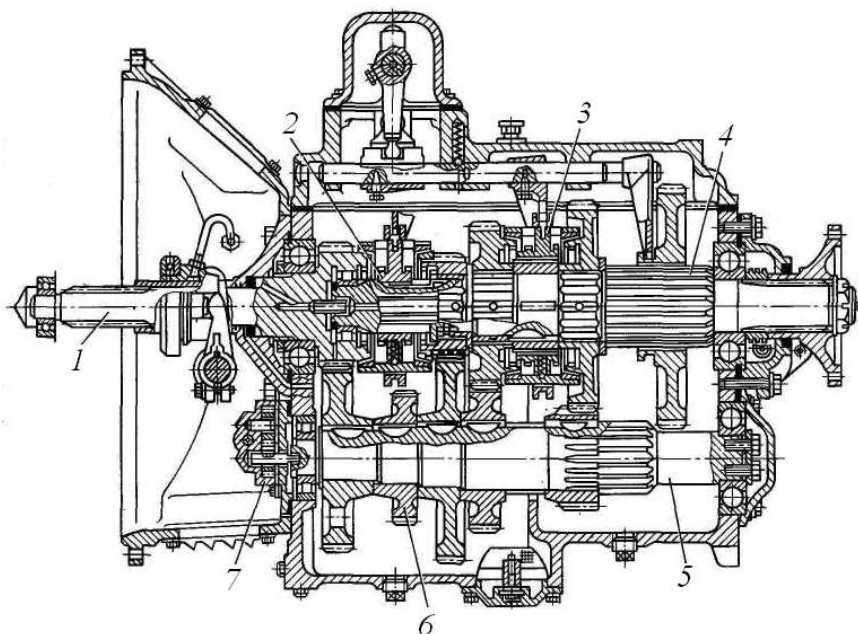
Пятиступенчатая трехвальная коробка передач автомобиля МАЗ-5335 [38]: 1 – ведущий вал; 2 – синхронизатор четвертой и пятой передач; 3 – синхронизатор второй и третьей передач; 4 – ведомый вал; 5 – промежуточный вал; 6 – шестерня отбора мощности; 7 – масляный насос
